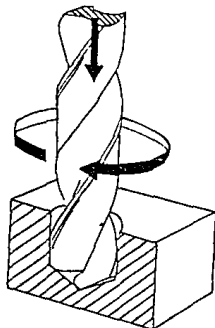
Movimiento al taladrar con la máquina de taladrar. a) Movimiento de corte o principal; b) Movimiento de avance
